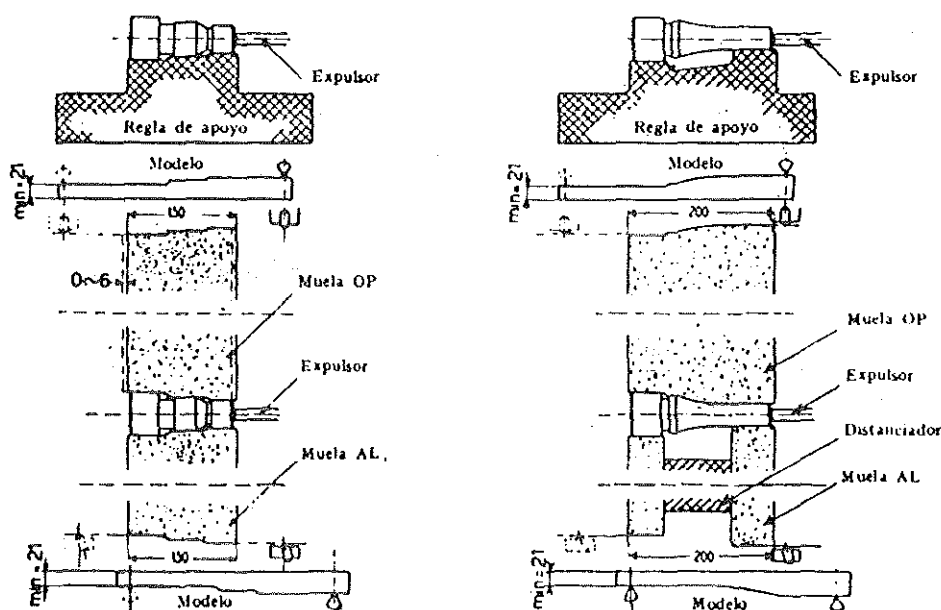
Retificação de peças com superfícies cilíndricas de diâmetros diversos.
